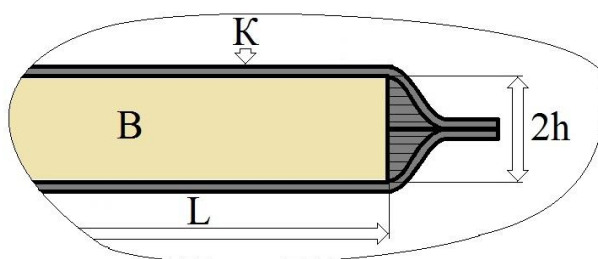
Геометрия технологической вставки для сварки конвертов: В – вставка; К – конверт теплообменника; L – длина прямолинейного участка входного канала пластины; 2h – высота вставки
